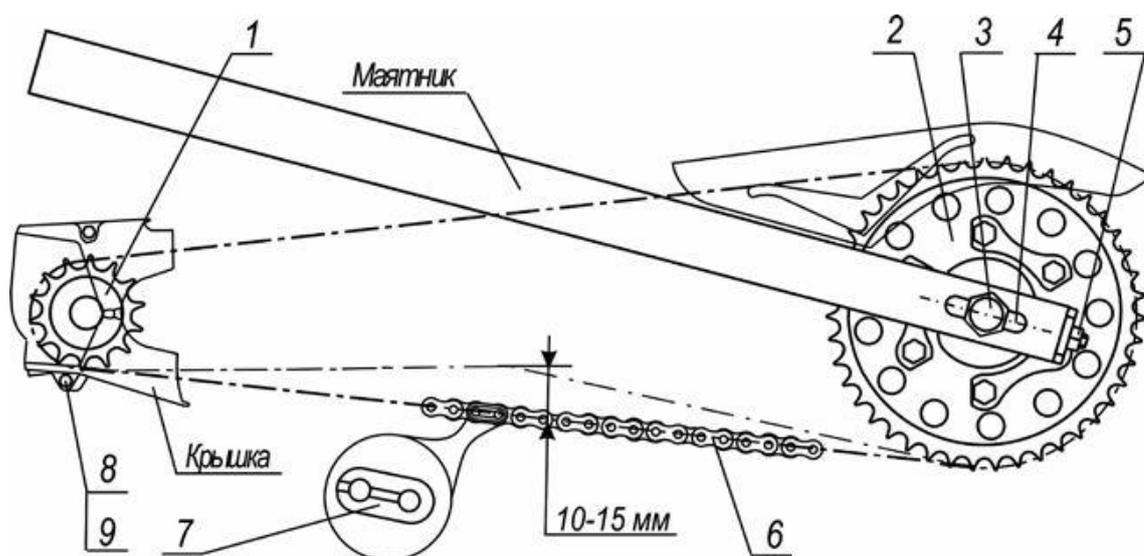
Главная передача мопеда. 1 - звездочка ведущая; 2 - звездочка ведомая; 3 – ось колеса; 4 – тяга оси; 5 – гайка тяги; 6 – цепь главной передачи; 7 - соединительное звено цепи; 8 – болт 9 - шайба
